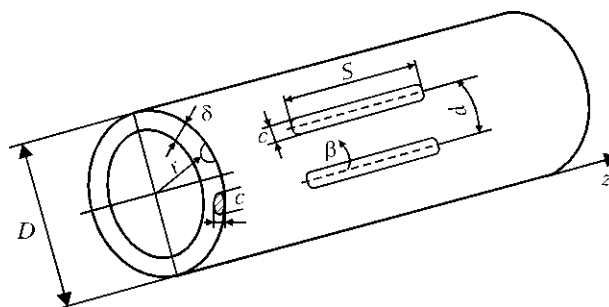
Схема цилиндрической оболочки-трубы с продольными канавочными дефектами утонения
